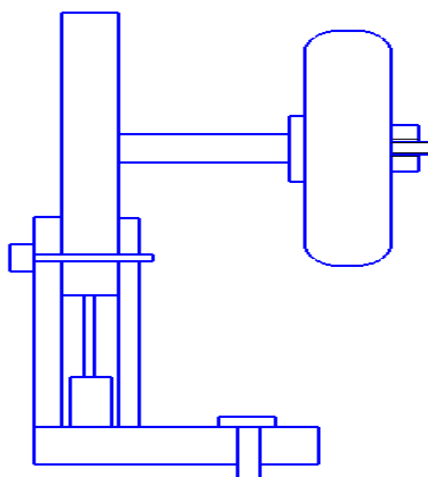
Второй вариант усовершенствование станда для шиномонтажа
